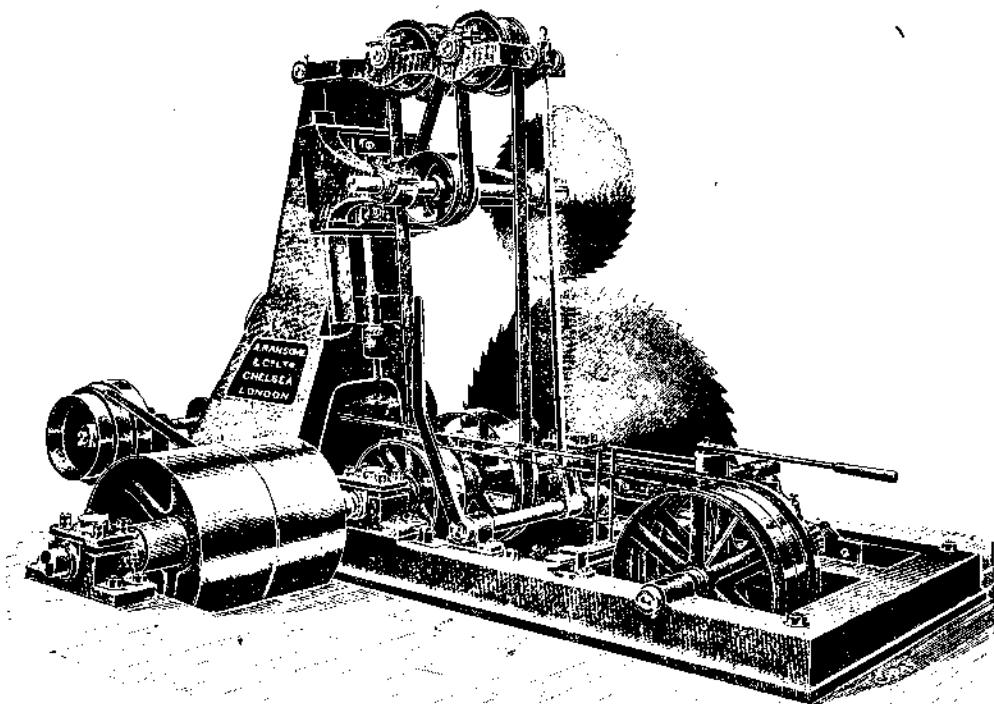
Лесопильный станок с двумя круглыми пилами.
